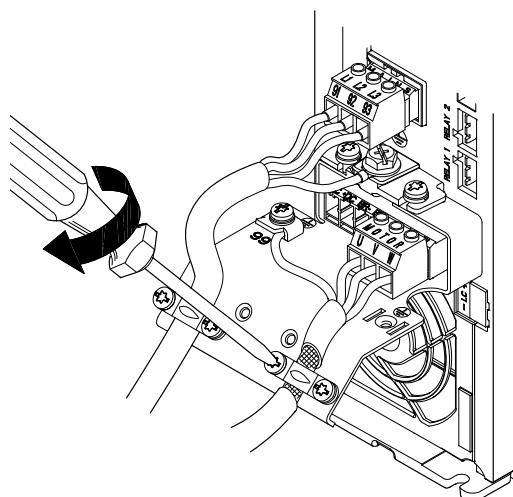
Branchement de la fiche moteur et fixation du câble blindé
